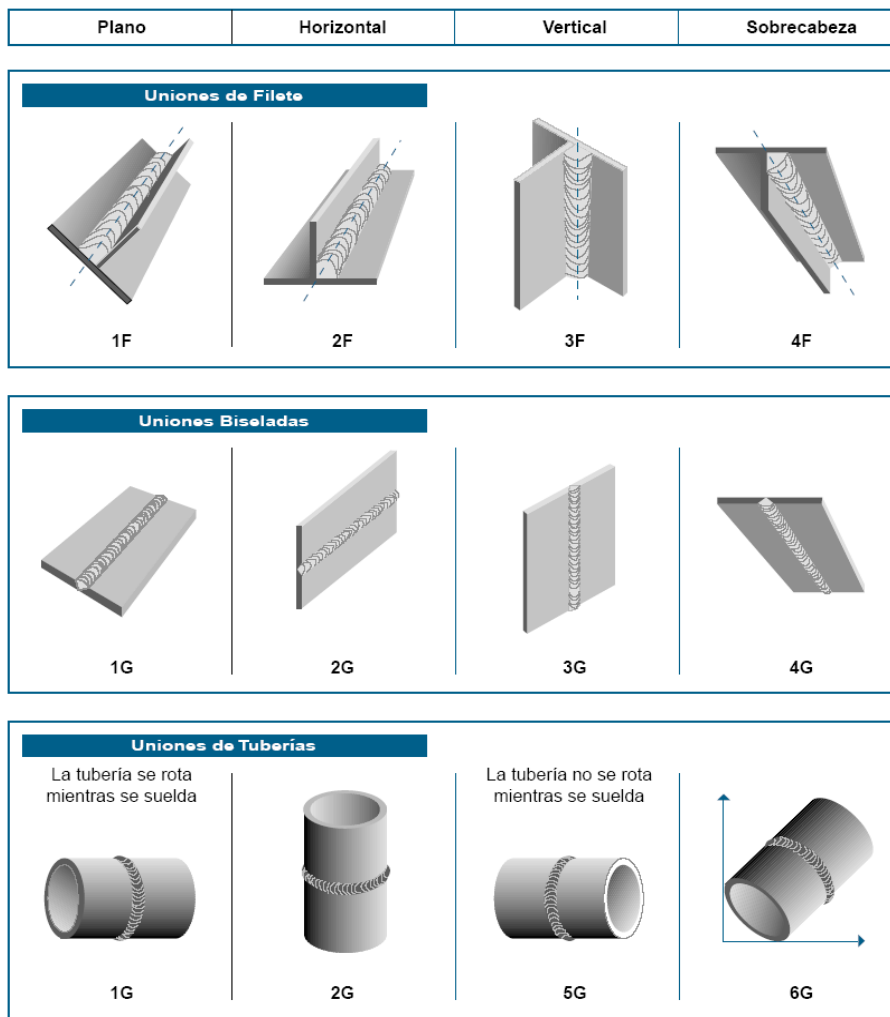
Posiciones de Soldadura
